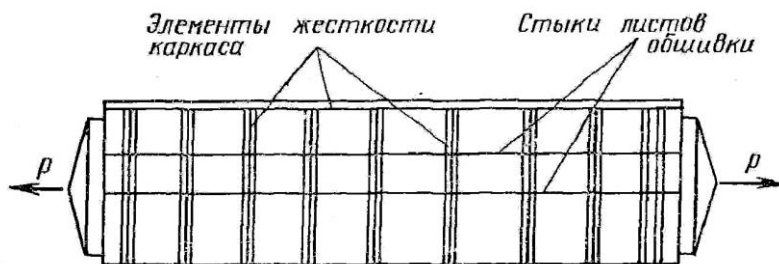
Схема приложения растягивающей силы при сварке листов обшивки с элементами жесткости
